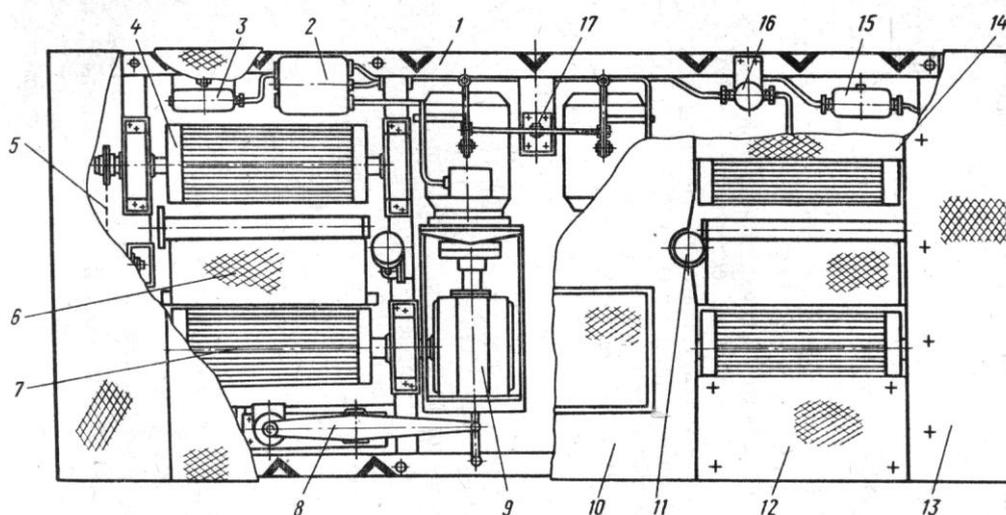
Схема тормозного стенда КИ-8944.
